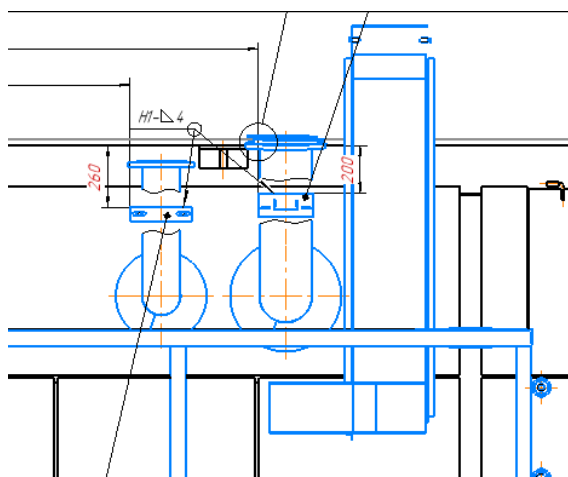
Предварительная схема размещения короба сброса с центрифуги
